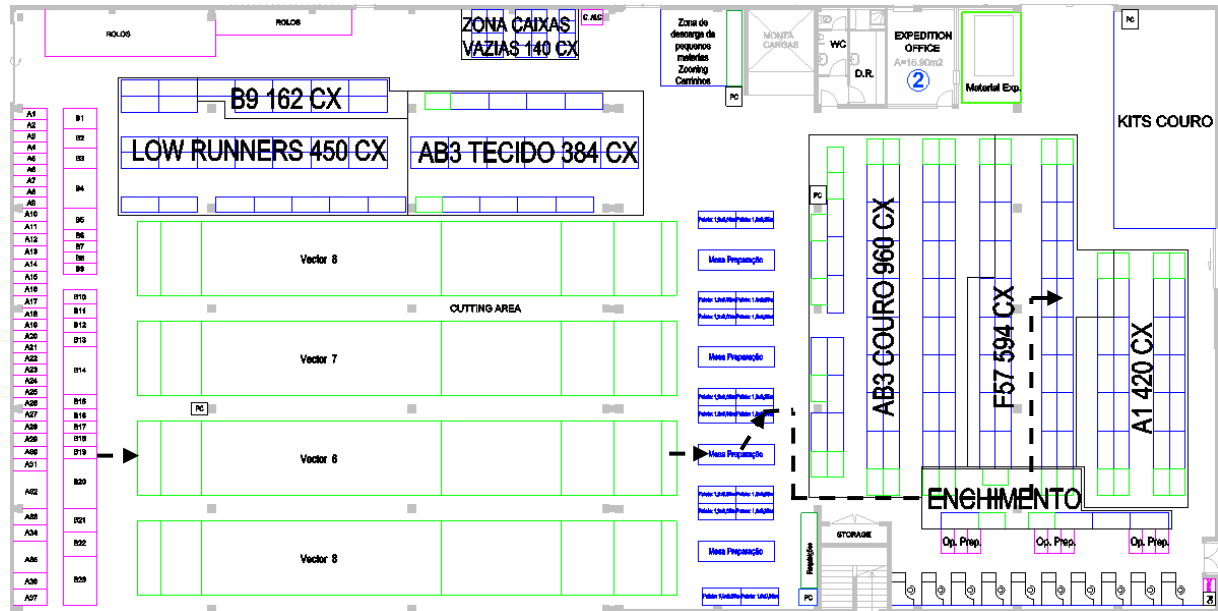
Segunda proposta layout - fluxo projeto Mini F57 s/enchimento
